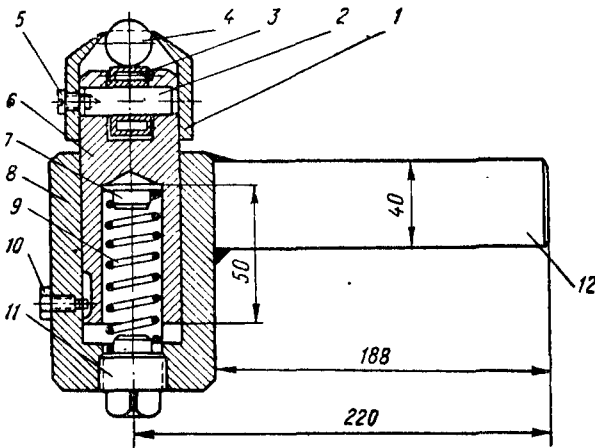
Шариковая накатка для обкатывания поверхностей.
